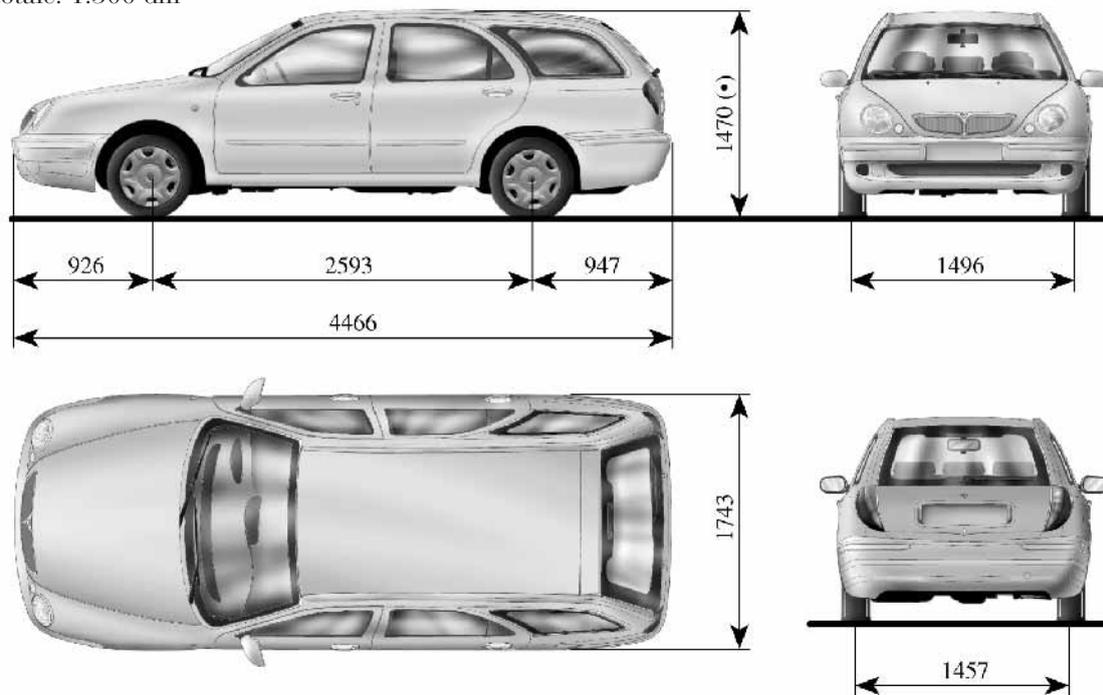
(•) Hauteur voiture avec barres porte-tout: 1578 mm
